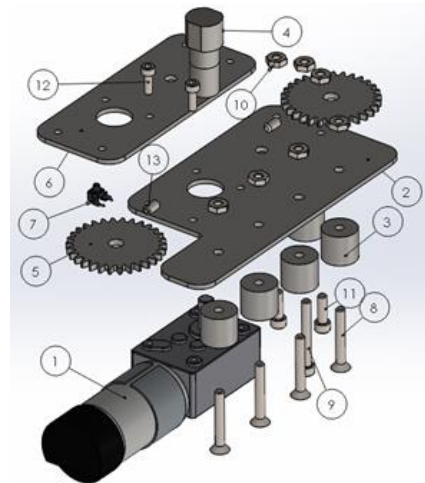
Sistema para giro de mordaza, posiciona el ángulo de corte.
